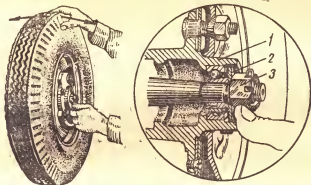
Регулировка подшипников ступицы переднего колеса:
